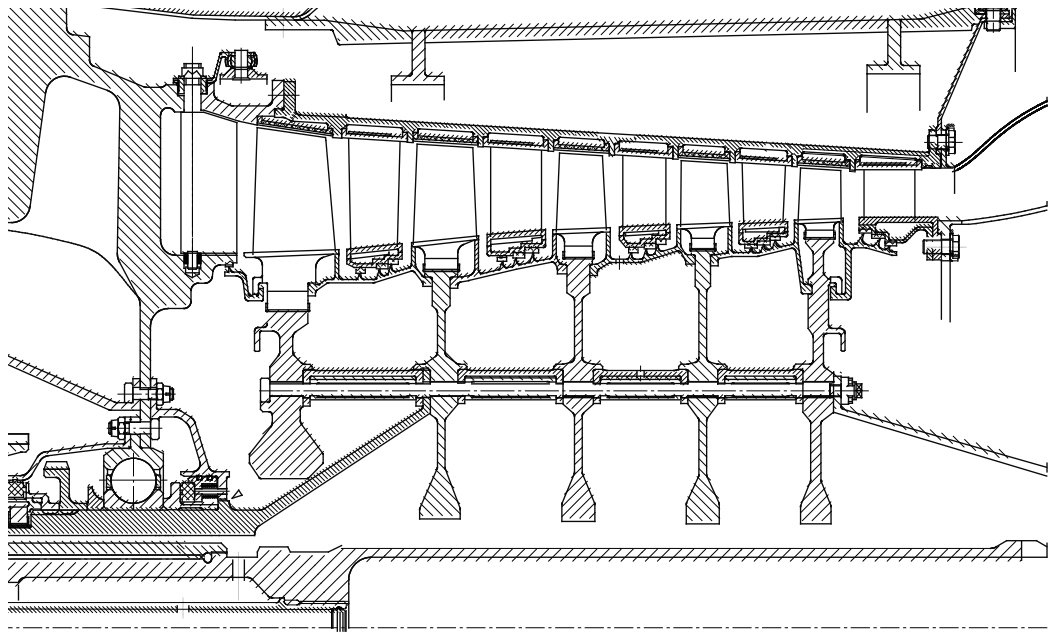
Ротор компрессора СД ТРДЦ АТФ3-6
